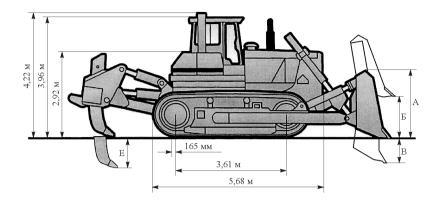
Бульдозерно-рыхлительный агрегат на базе гусеничного трактора
